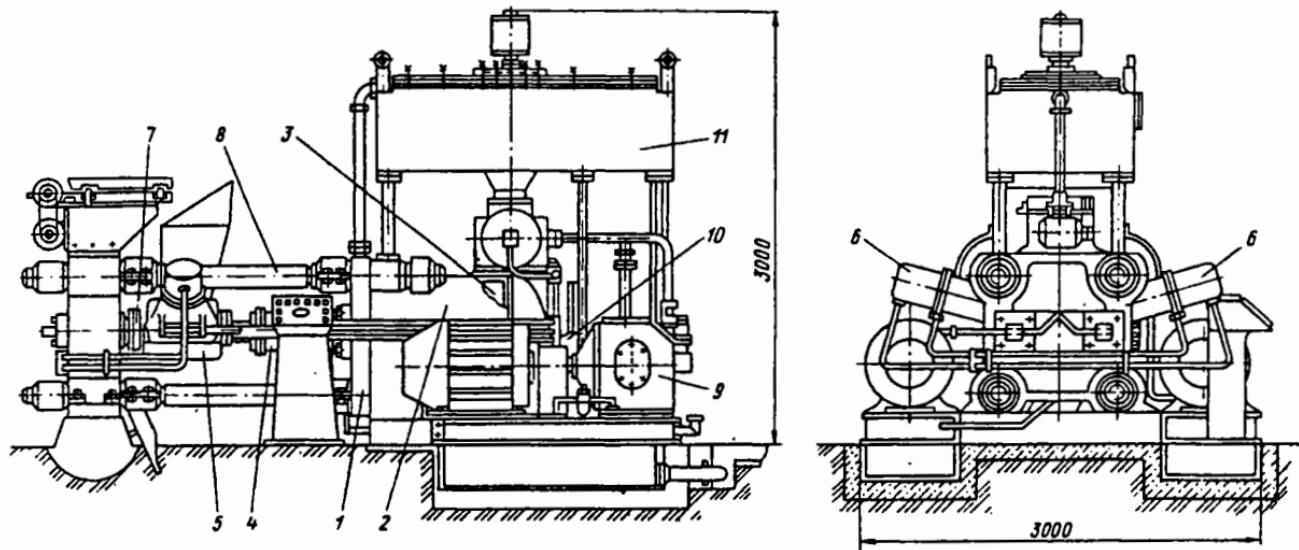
Пресс модели Б 6238 для брикетирования стружки: 1 — станина; 2 — главный цилиндр; 3 — поршень; 4 — штампель; 5 — контейнер; 6 — трамбовка; 7 — матрица; 8 — стяжные шпильки; 9 — масляный насос; 10 — вспомогательный цилиндр; 11 — масляный бак
